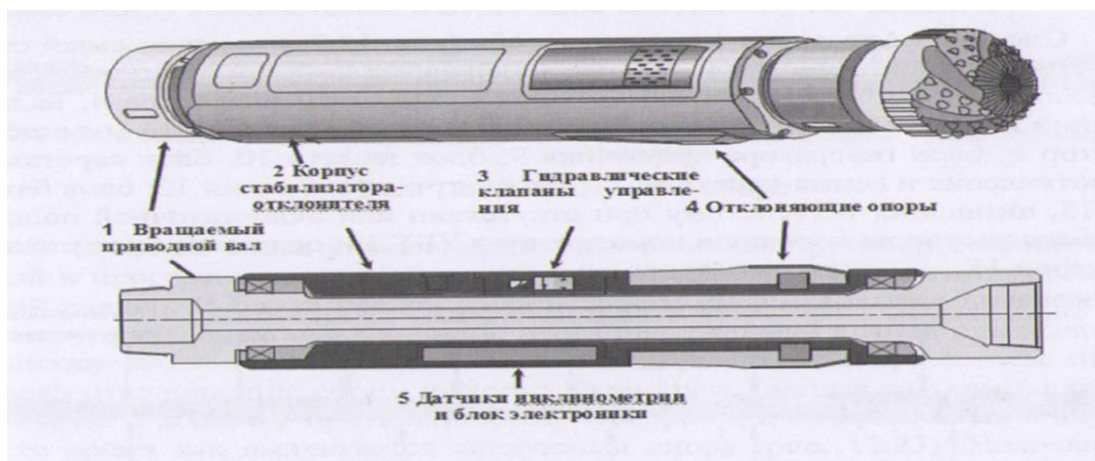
Невращающийся стабилизатор-отклонитель.
